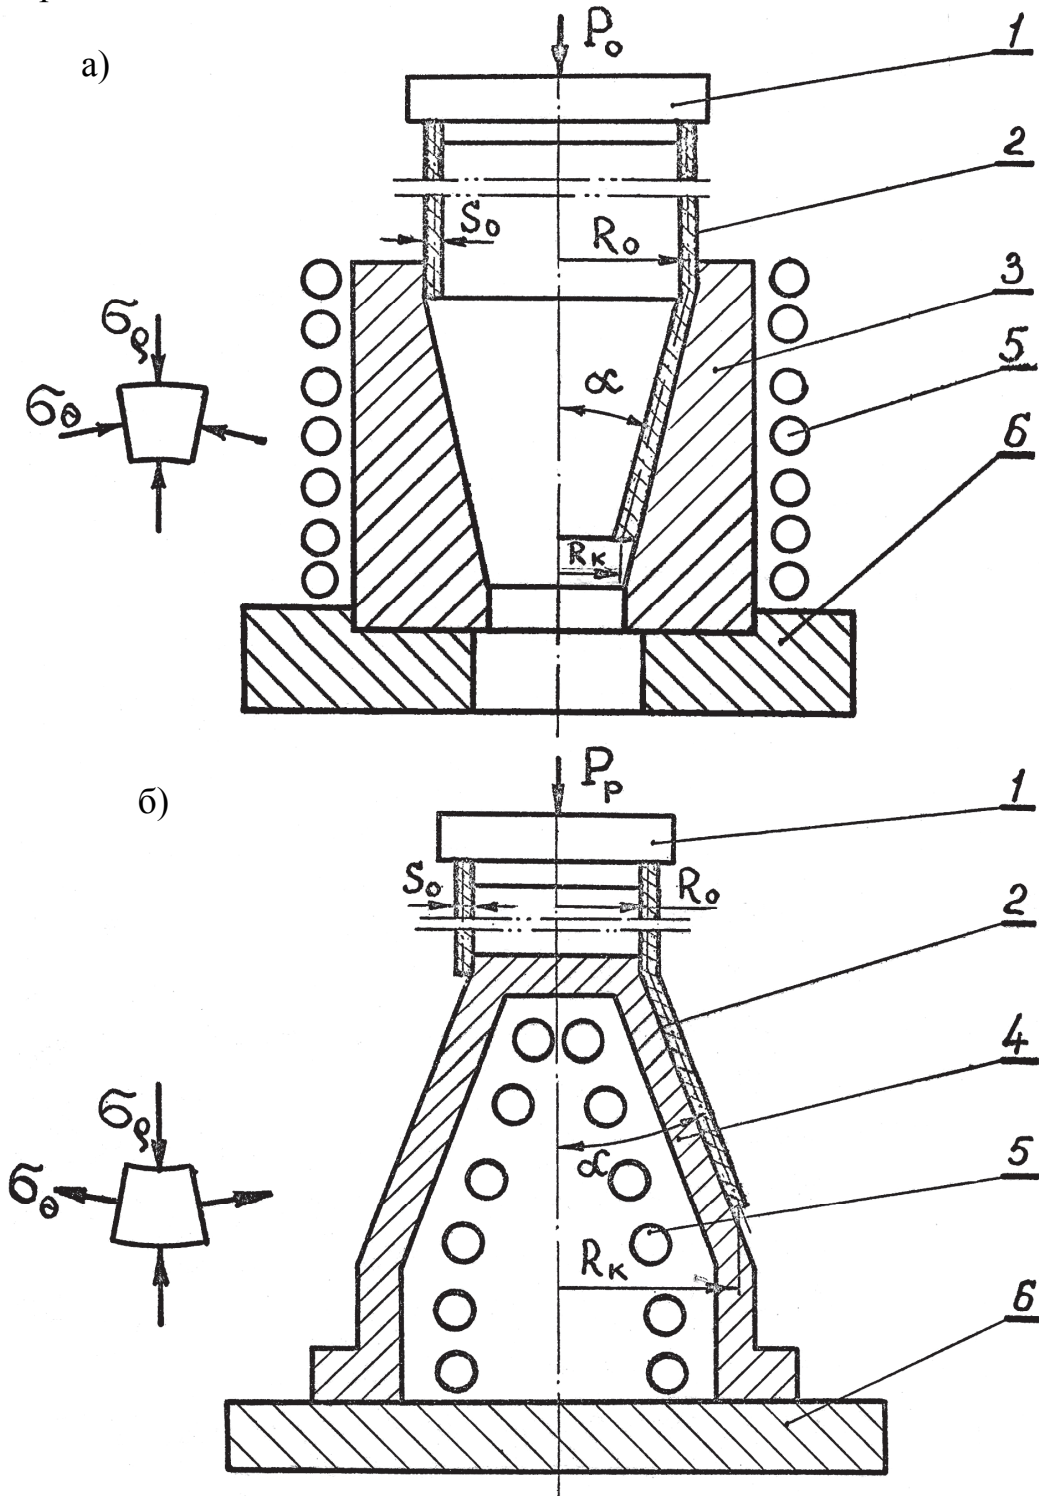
Схемы обжима (а) и раздачи (б) трубчатых заготовок:
